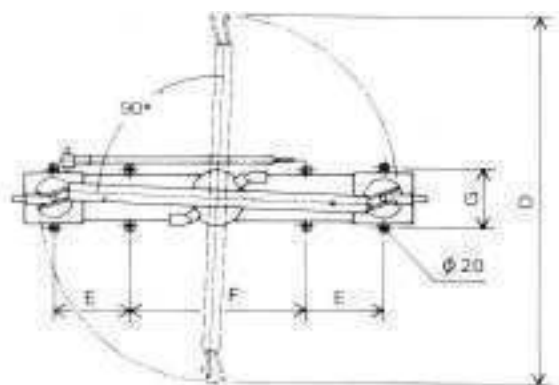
Seccionador columna giratoria central y cuchillas puestas a tierra.
